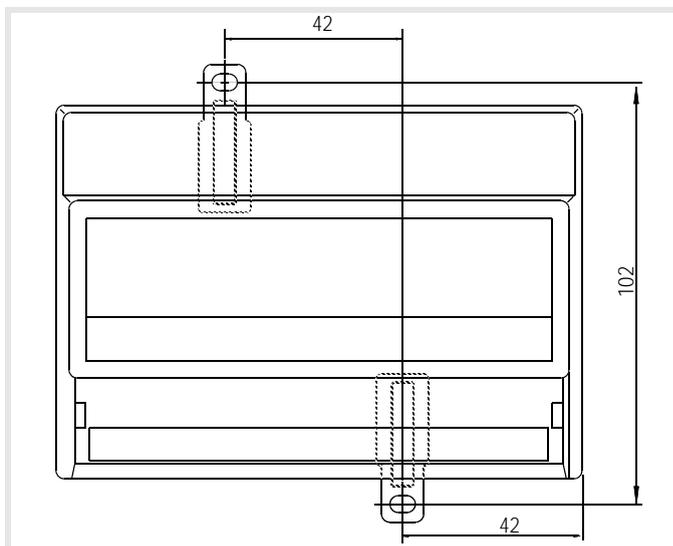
Maßzeichnung für Wandmontage (Frontansicht)
